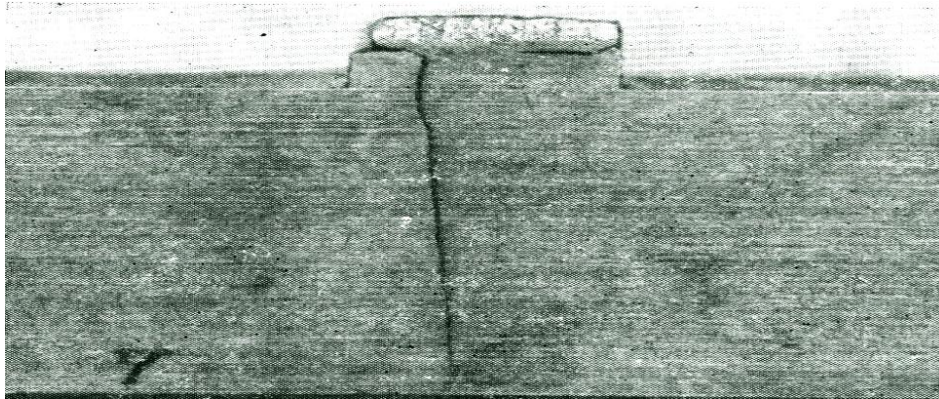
Образец сварного соединения. Усталостная трещина на образце сварной прямошовной трубы диаметром 1240 мм
